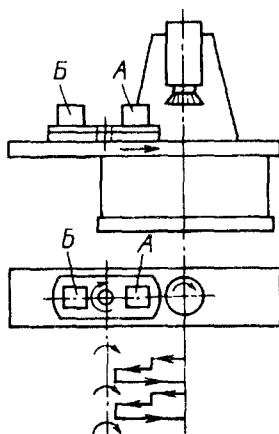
Схема обработки деталей с помощью поворотного стола
